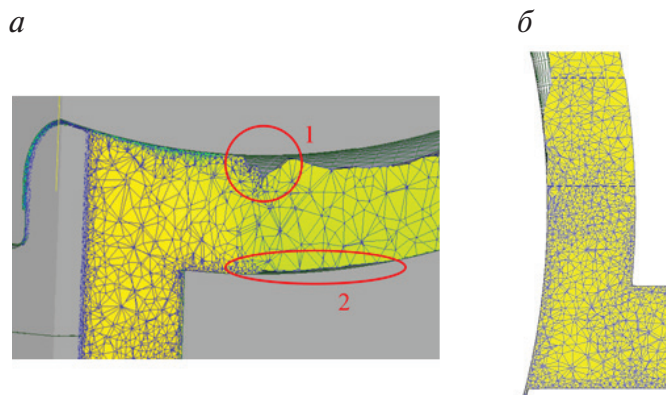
Складки металла при распрессовке заготовки в желобе колеса:
